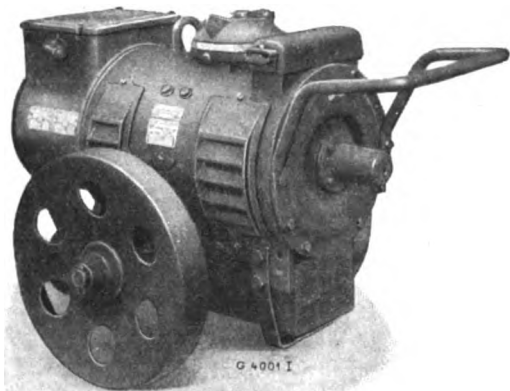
Schweißumformer mit freiem Wellenende für einen Regelbereich von 50 bis 300 A.
